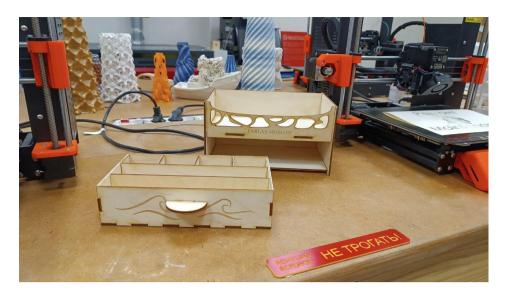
Полученные элементы органайзера с помощью лазерного станка
